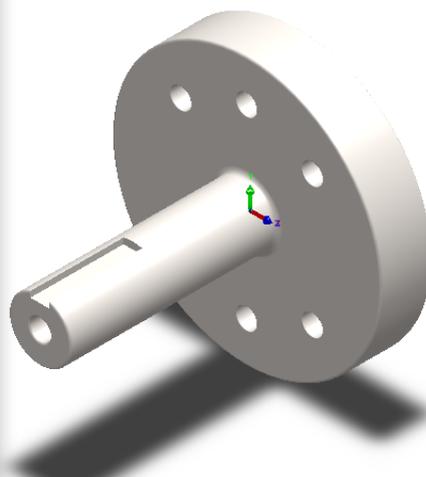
Propiedades geométricas del acoplamiento al motor. Fuente: captura de SolidWorks.
